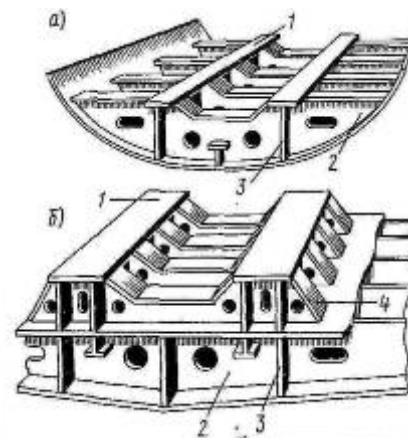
Фундаменты: а — фундамент главного двигателя на одинарном дне; б — то же, на двойном дне. 1 — опорные горизонтальные полосы; 2 — флор; 3— днищевой стрингер; 4—кницы с полками.
